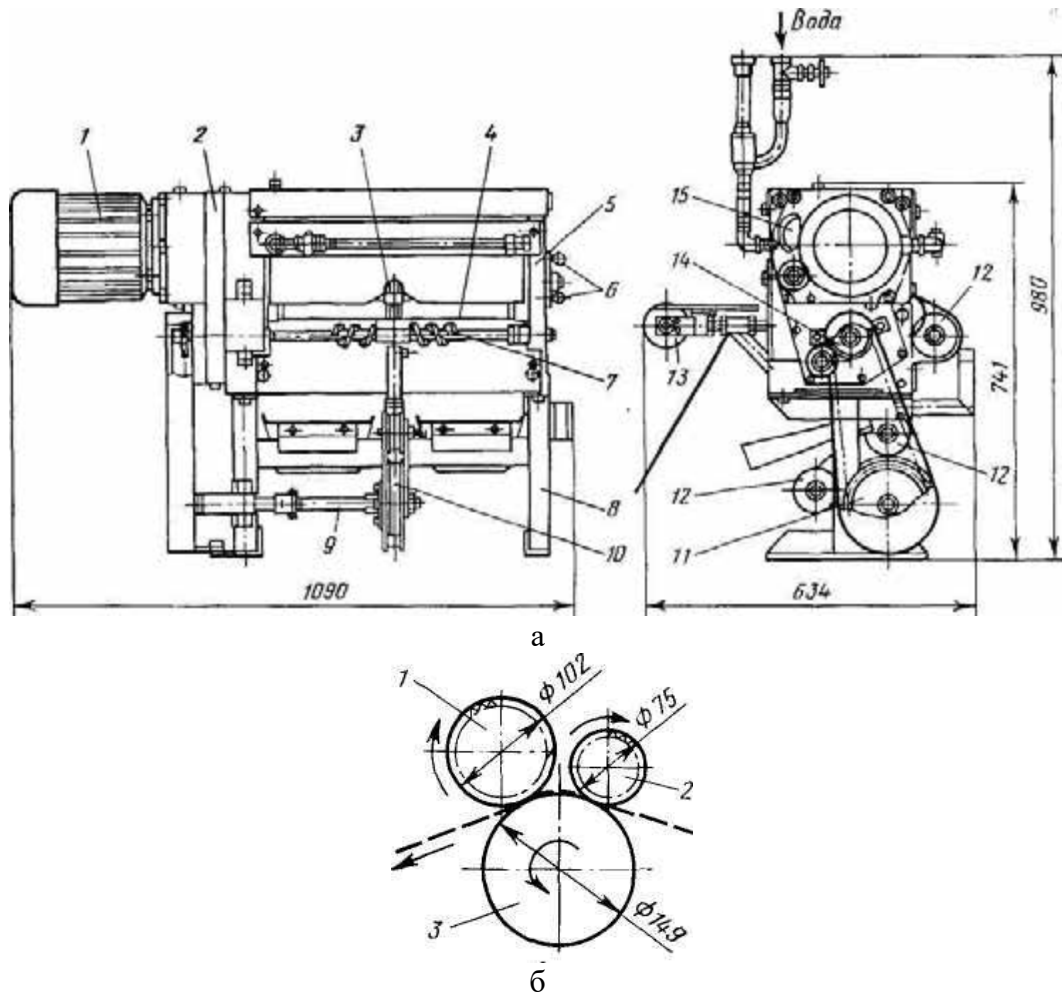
Відтискні вальці В2-ФКП-1: а – загальний вигляд: 1 – електродвигун, 2 – редуктор; 3, 15 – рифлені валики; 4 – гладенький валик; 5 – стійка; 6 – рукоятки; 7 – шнековий роздільник; 8 – рама; 9 – вал; 10 – приводний шків транспортера; 11, 14 – зірочки ланцюгової передачі; 12 – оборотні шків; 13 – натяжний шків; б – технологічна схема: 1,2 – рифлені вальці; 3 – гладенький валик
